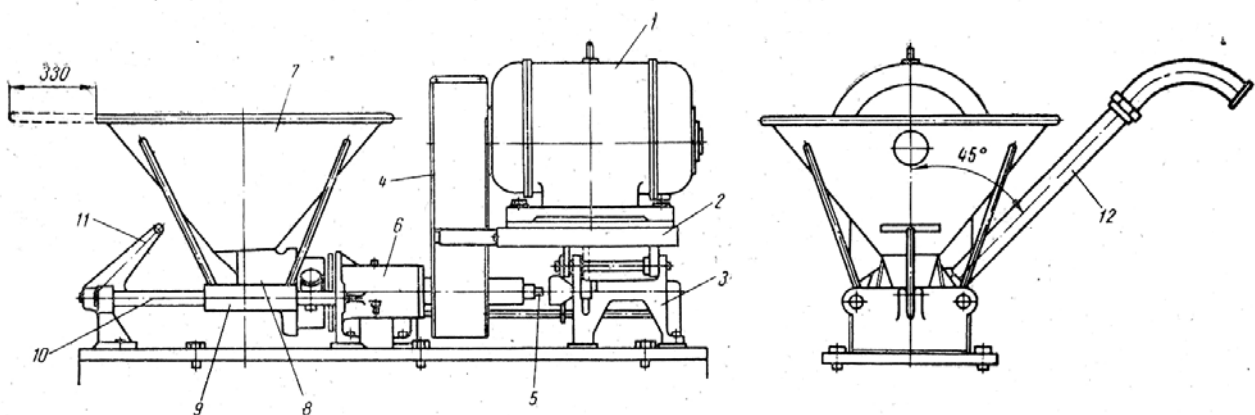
Схема емульситатора ANCO: 1 – електродвигун; 2 – плита; 3 – стойка; 4 – клинопасова передача; 5 – штанга; 6 – корпус; 7 – приймальний бункер; 8 – горловина; 9 – муфти; 10 – направляючі; 11 – важіль; 12 – розвантажувальний рукав
